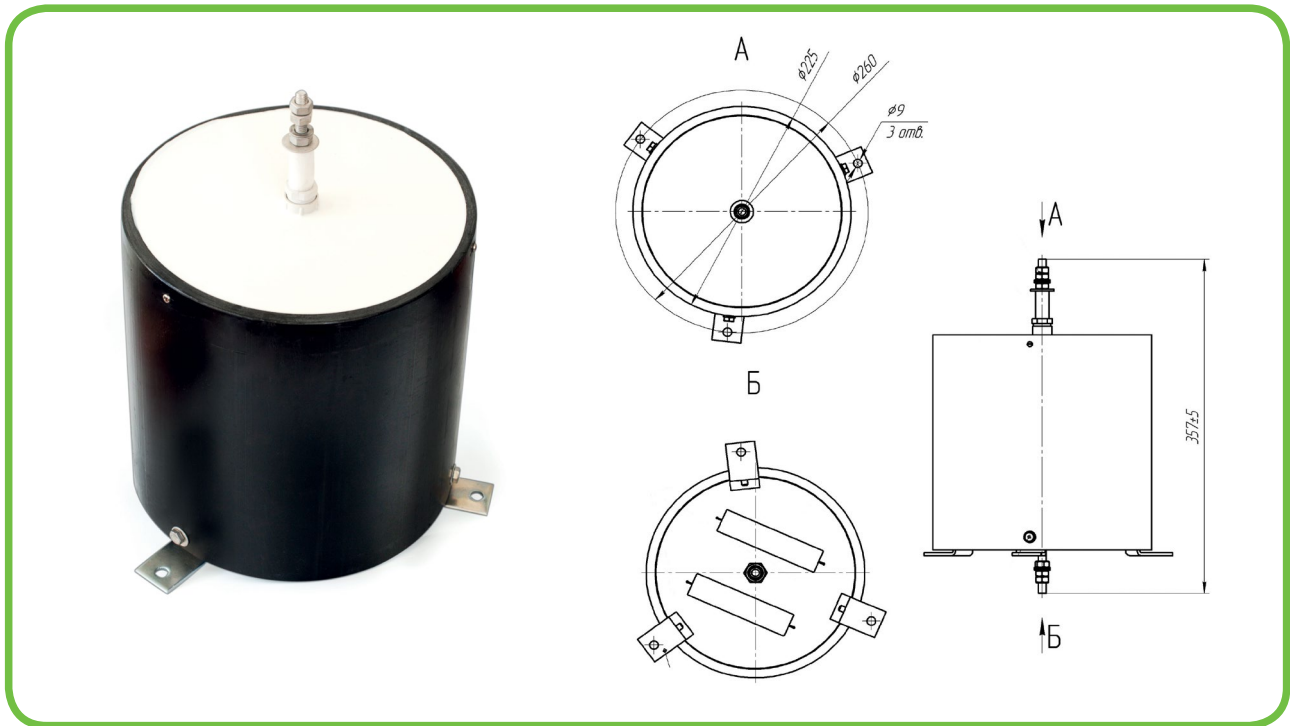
Общий вид и габаритные размеры элемента настройки универсального
